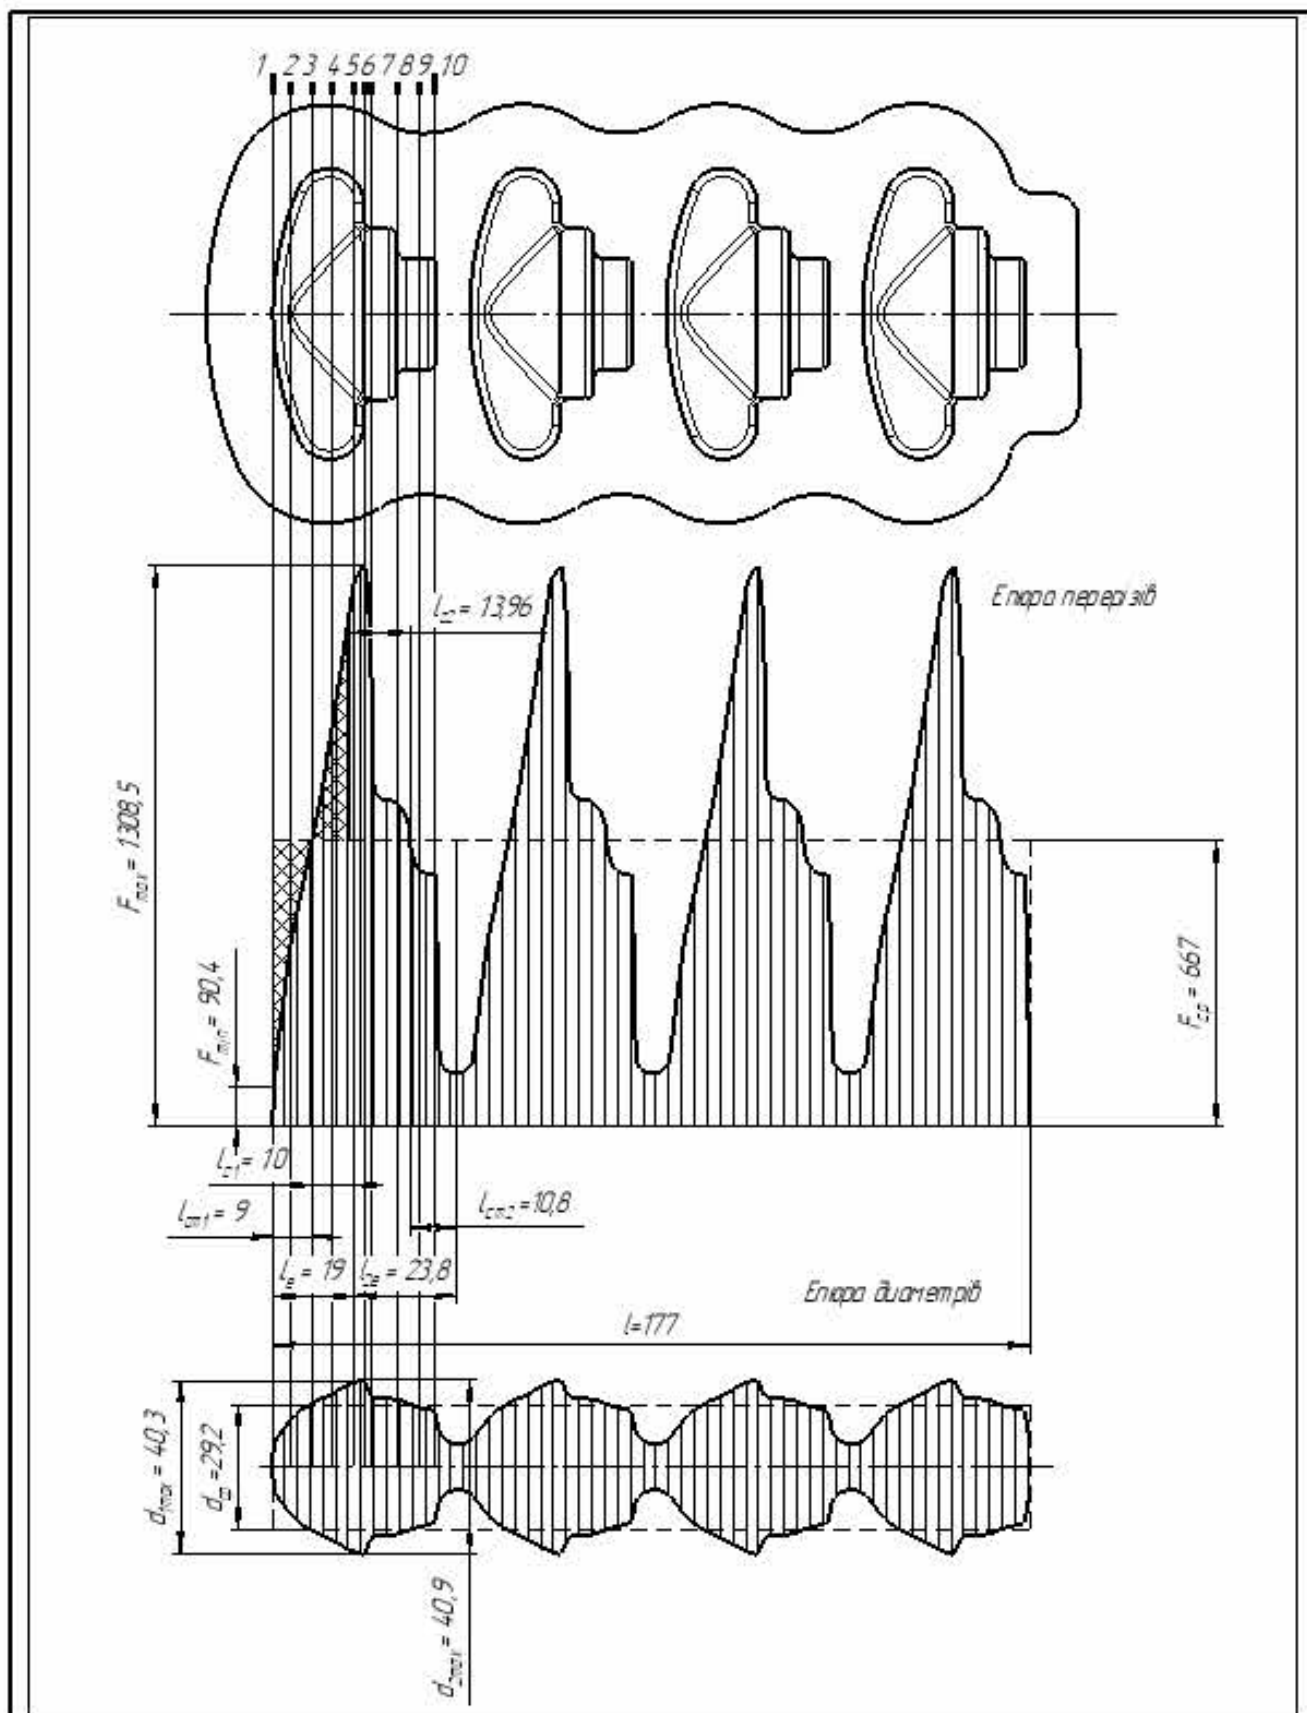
Побудова розрахункової заготовки та епюри перерізів
